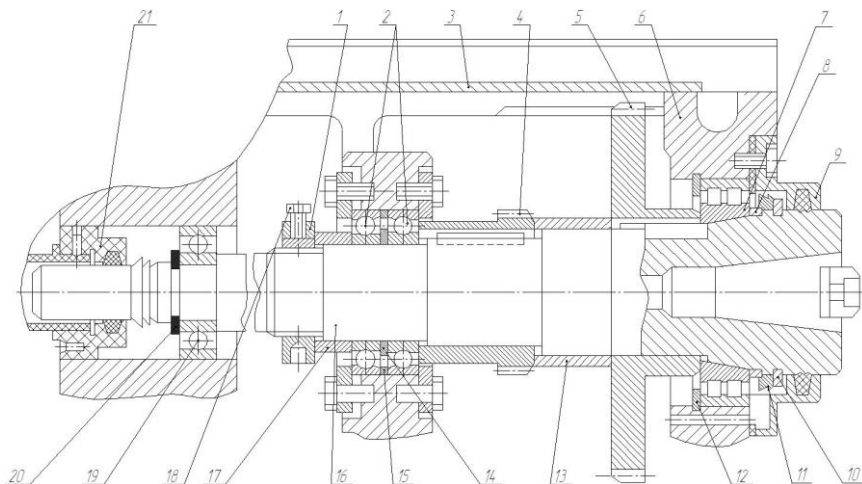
Горизонтальный шпиндельный узел станка мод 6М82
